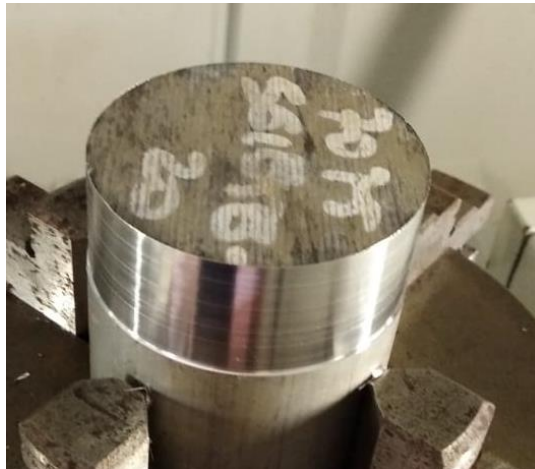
Proceso de cilindrado. Fuente: Autor
